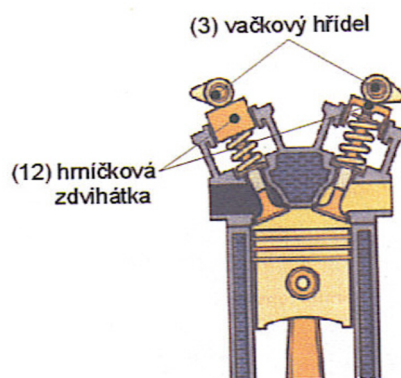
Rozvod OHC (Over Head Camshaft) [3].
